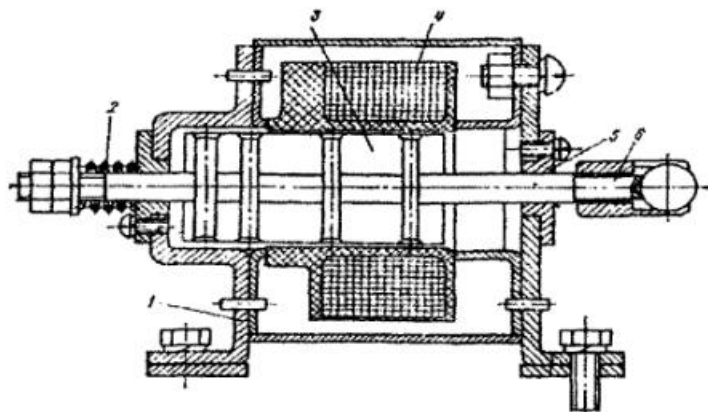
Ескіз пристрою для чеканки поверхні деталі
